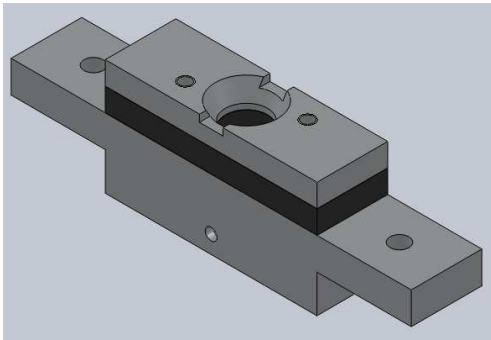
konstruktive Darstellung der unteren Grundkonstruktion
